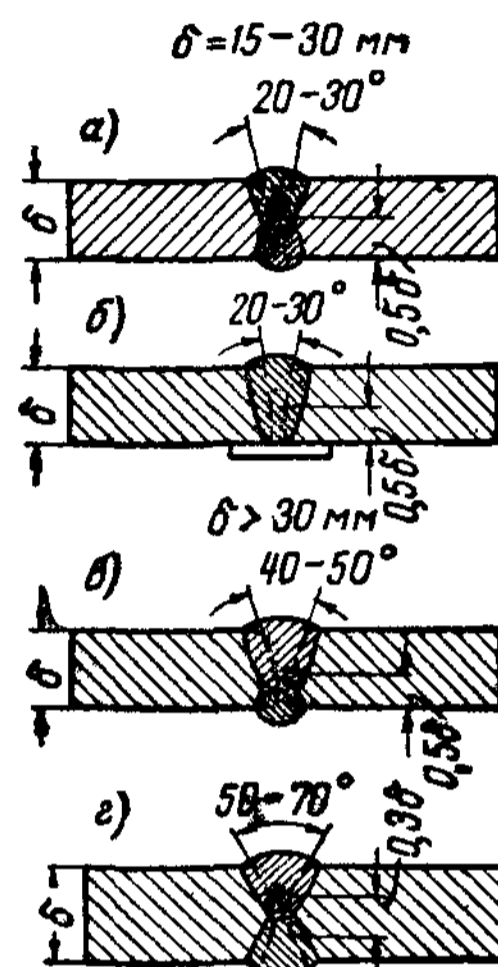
Разделка листов под стыковой шов при автоматической сварке
